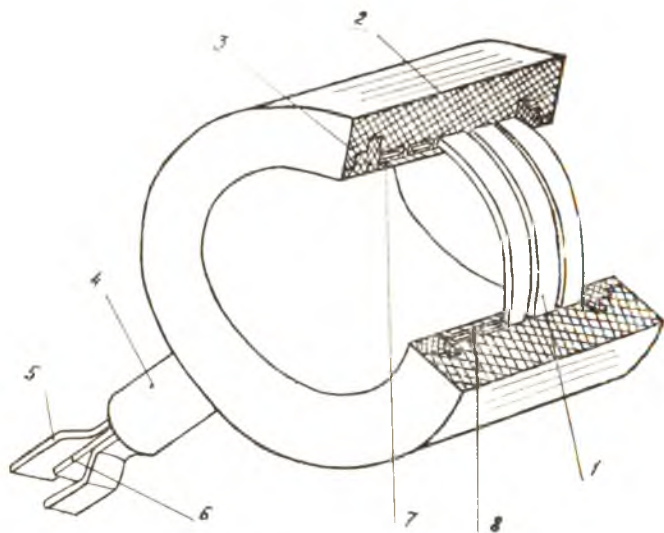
Многовитковый индуктор для обжима трубчатых заготовок: 1 — токопровод, 2 — корпус, 3 — фланец, 4 — бандаж, 5 — токоподвод, 6 — прокладка, 7 — главная изоляция, 8 — витковая изоляция
